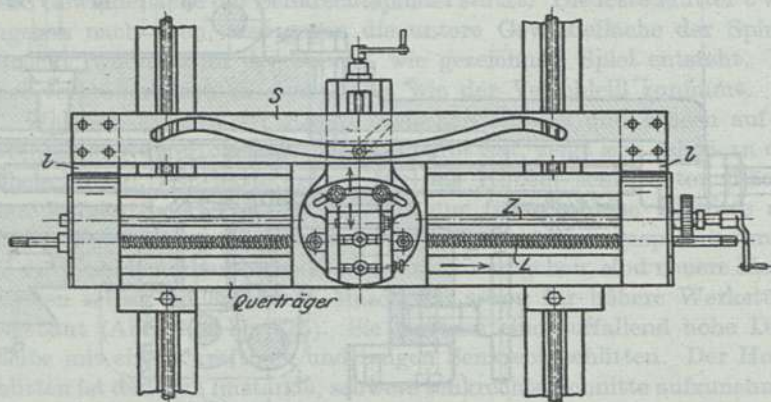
Hobelschlitten mit Lehre. Brune, G. m. B. H., Köln.
